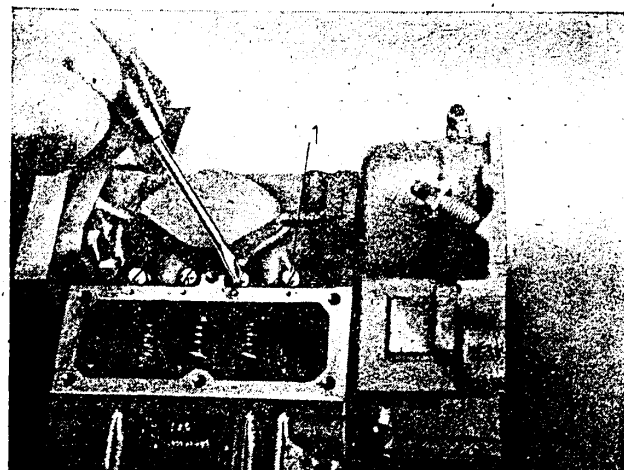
Rollenstößelführungsschrauben (1) lösen
